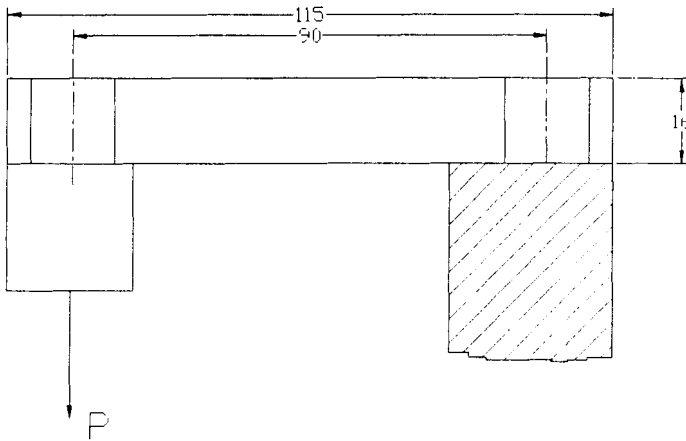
Platina de Soporte, junta empernada extremo izquierdo
